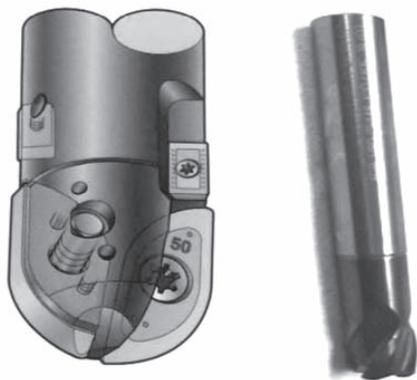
a) Herramienta de plaquetas, fresa de tipo esférico. b) Fresa integral con radio de punta, denominada tórica (derecha)
